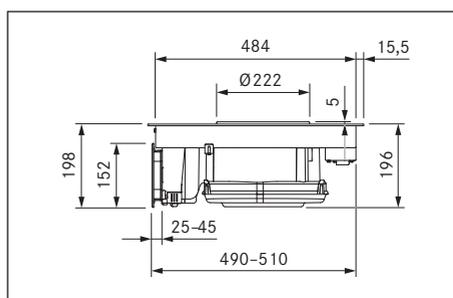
BHU dimensioni apparecchio vista laterale
